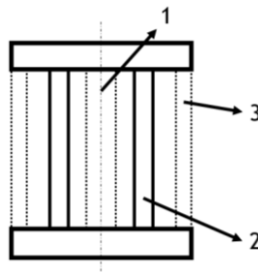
Configuração estrutural da ligação entre seções da asa do Crossover
